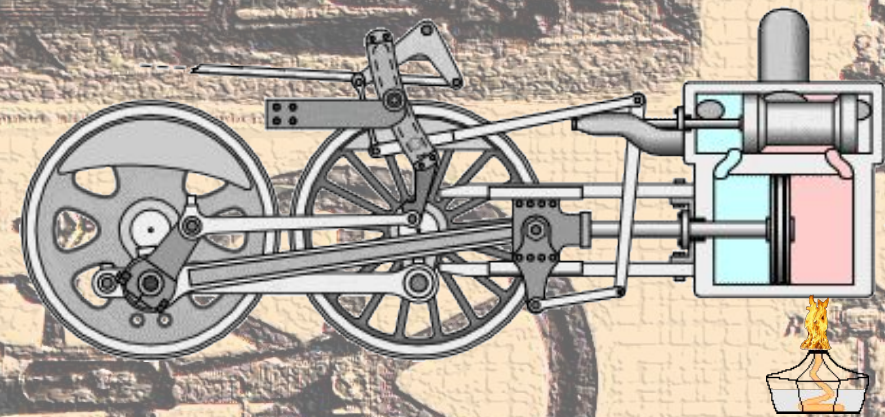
Паровый двигатель с вертикальным цилиндром и трубой.
